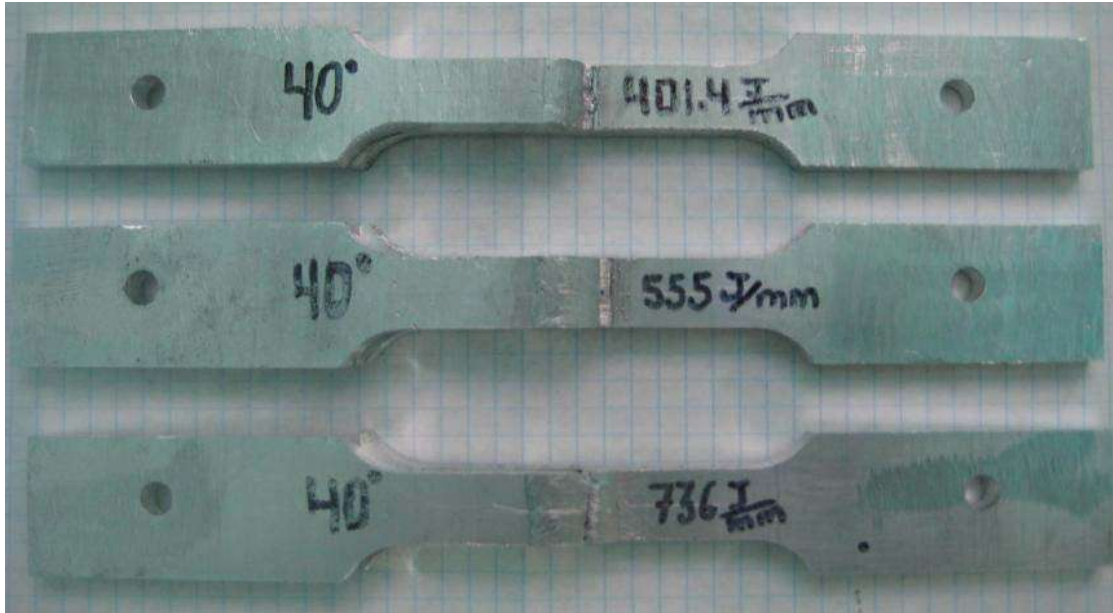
Probetas fracturadas de soldaduras realizadas con un ángulo de 40°
